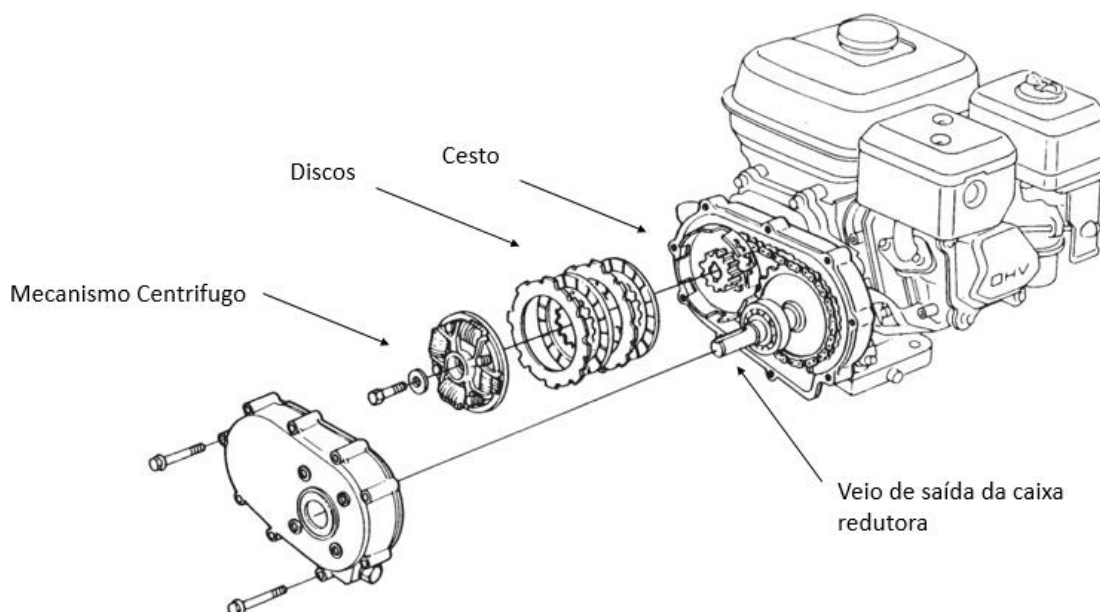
Vista explodida da caixa redutora com embraiagem dos motores Honda GX120/160 (adaptado de [12]).
